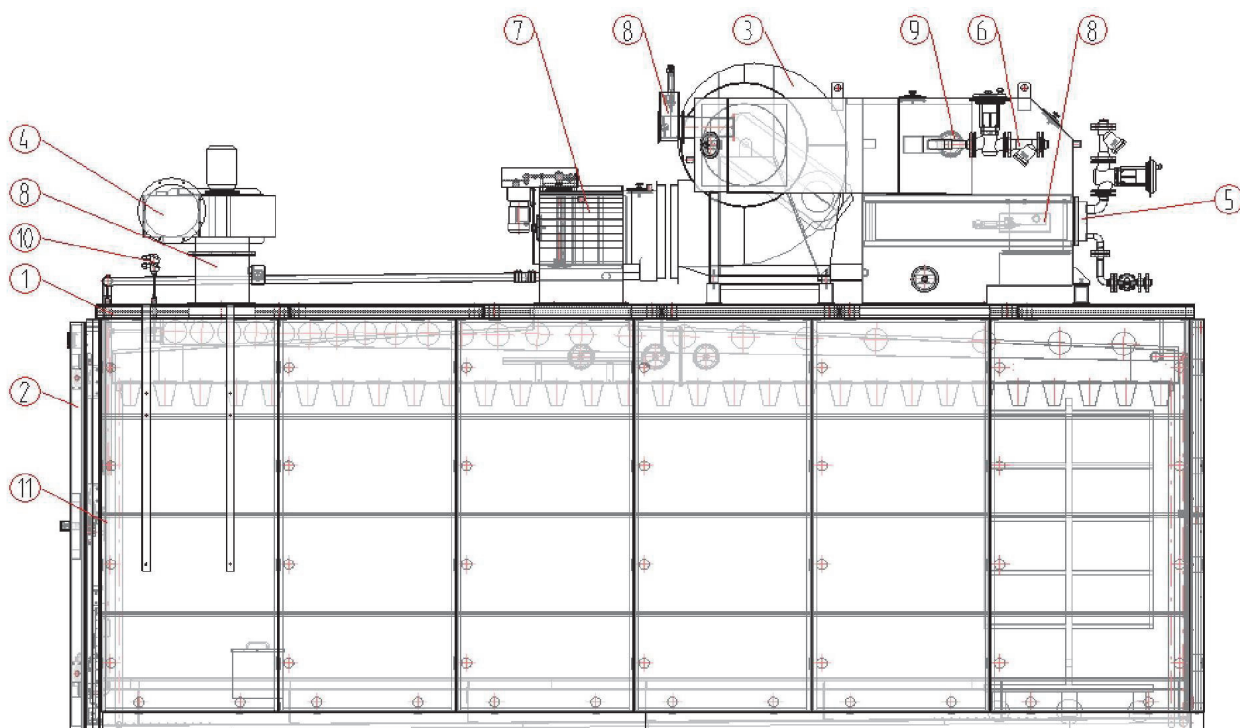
Общий вид термокамеры Vemag AEROMAT: 1 – корпус; 2 – дверь; 3 – циркуляционный вентилятор; 4 – вытяжной вентилятор; 5 – нагревательный элемент; 6 – увлажняющий элемент; 7 – заслонка; 8 – запорные клапаны; 9 – крышка люка техобслуживания; 10 – измерительное устройство; 11 – датчик температуры внутри продукта
